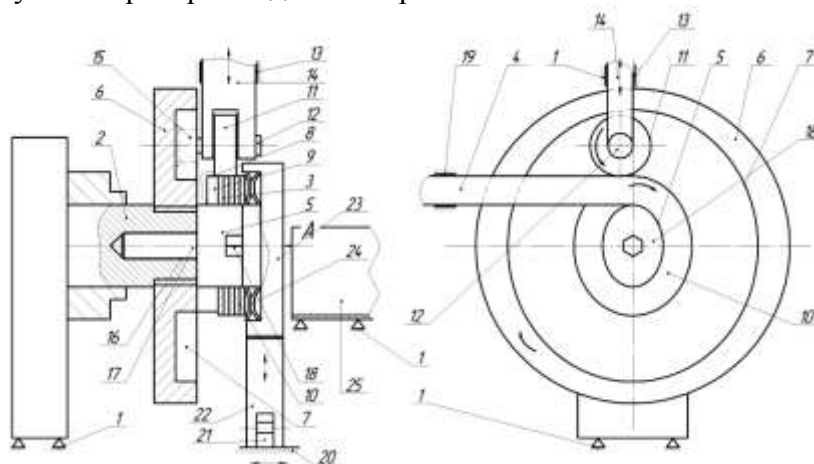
Пристрій для навивання профільних гвинтових заготовок
